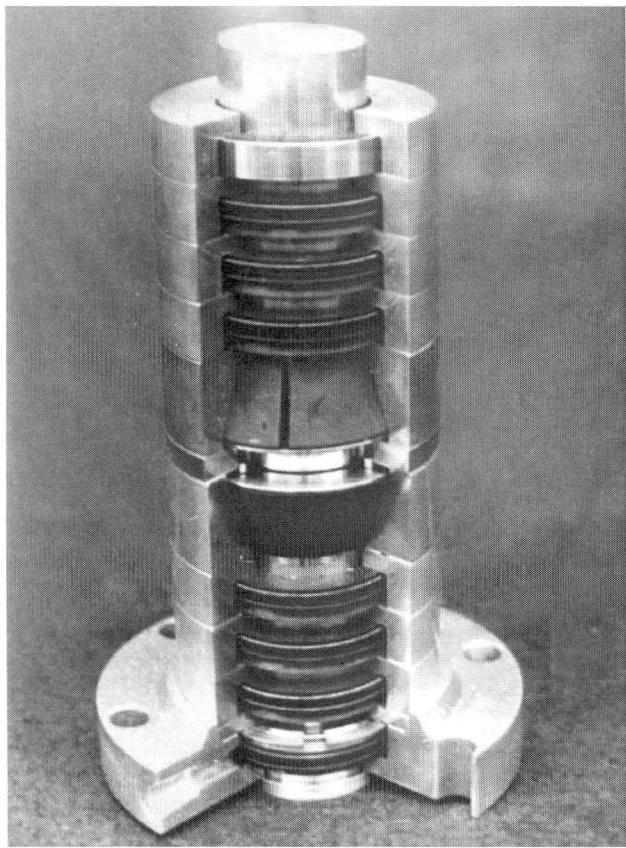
Устройство уплотнения штока без смазки с теплосъемными коническими элементами
